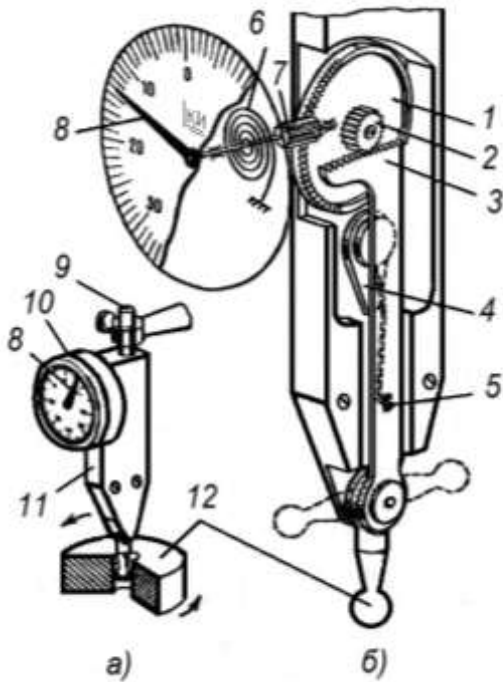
Индикатор ИРБ рычажно-зубчатый с боковой шкалой: а – общий вид; б – конструктивная схема
